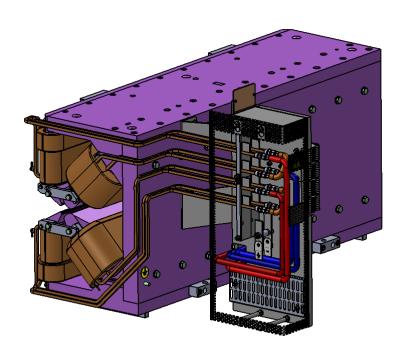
Эскизный вид диполь-квадрупольного магнита
